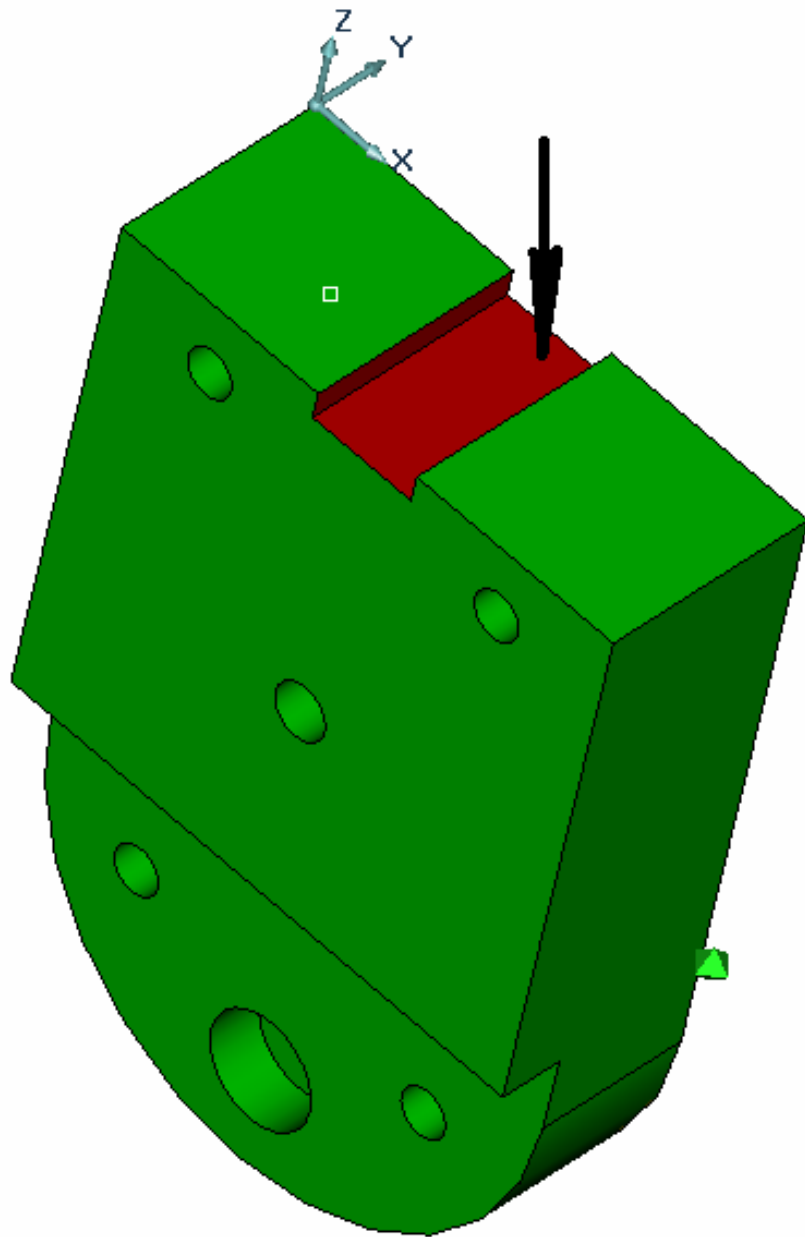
Модель обработки по завершающей фрезерной операции 015
